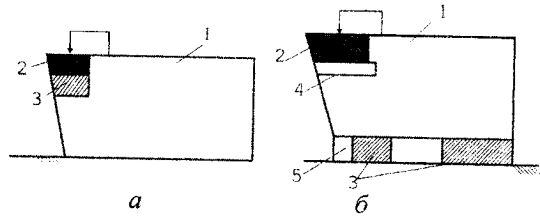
Схеми установки пластин для демпфірування автоколивань у різальному інструменті (а – під різальним елементом; б – під державкою): 1 – державка; 2 – різальна пластина; 3 – пластина для демпфірування автоколивань; 4 – пластина із твердого сплава; 5 – сепаратор
